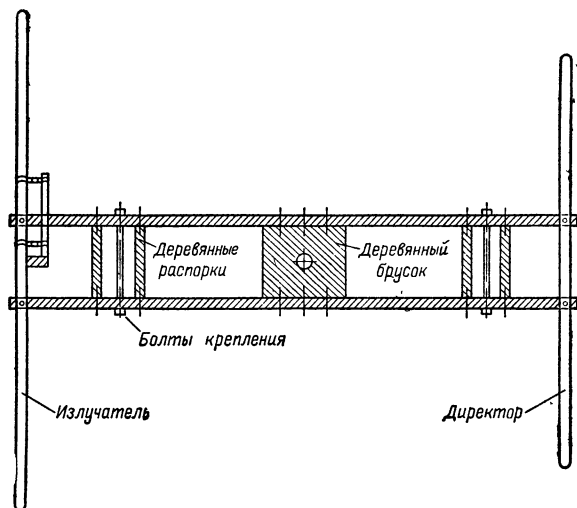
Конструкция деревянной траверсы для двух-элементного направленного излучателя.
